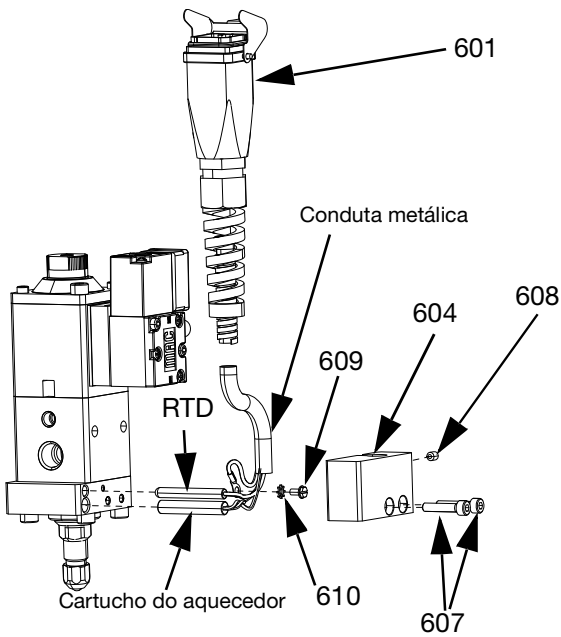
Conjunto do aquecedor para bloco de saída de 0 mm
